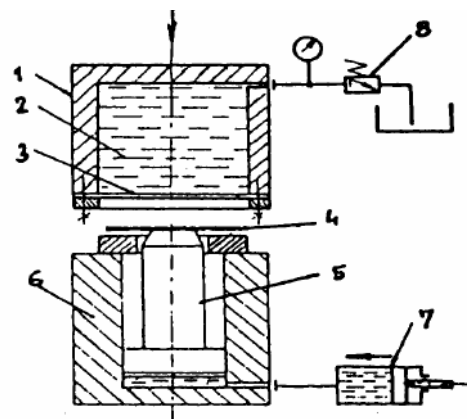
tažný nástroj pro tažení pryží systém Guérin [6]
